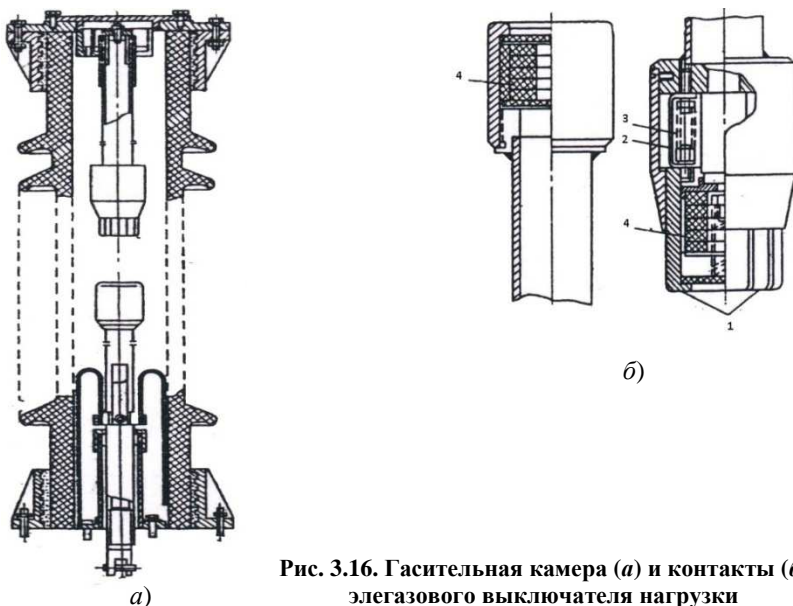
Гасительная камера (а) и контакты (б) элегазового выключателя нагрузки
